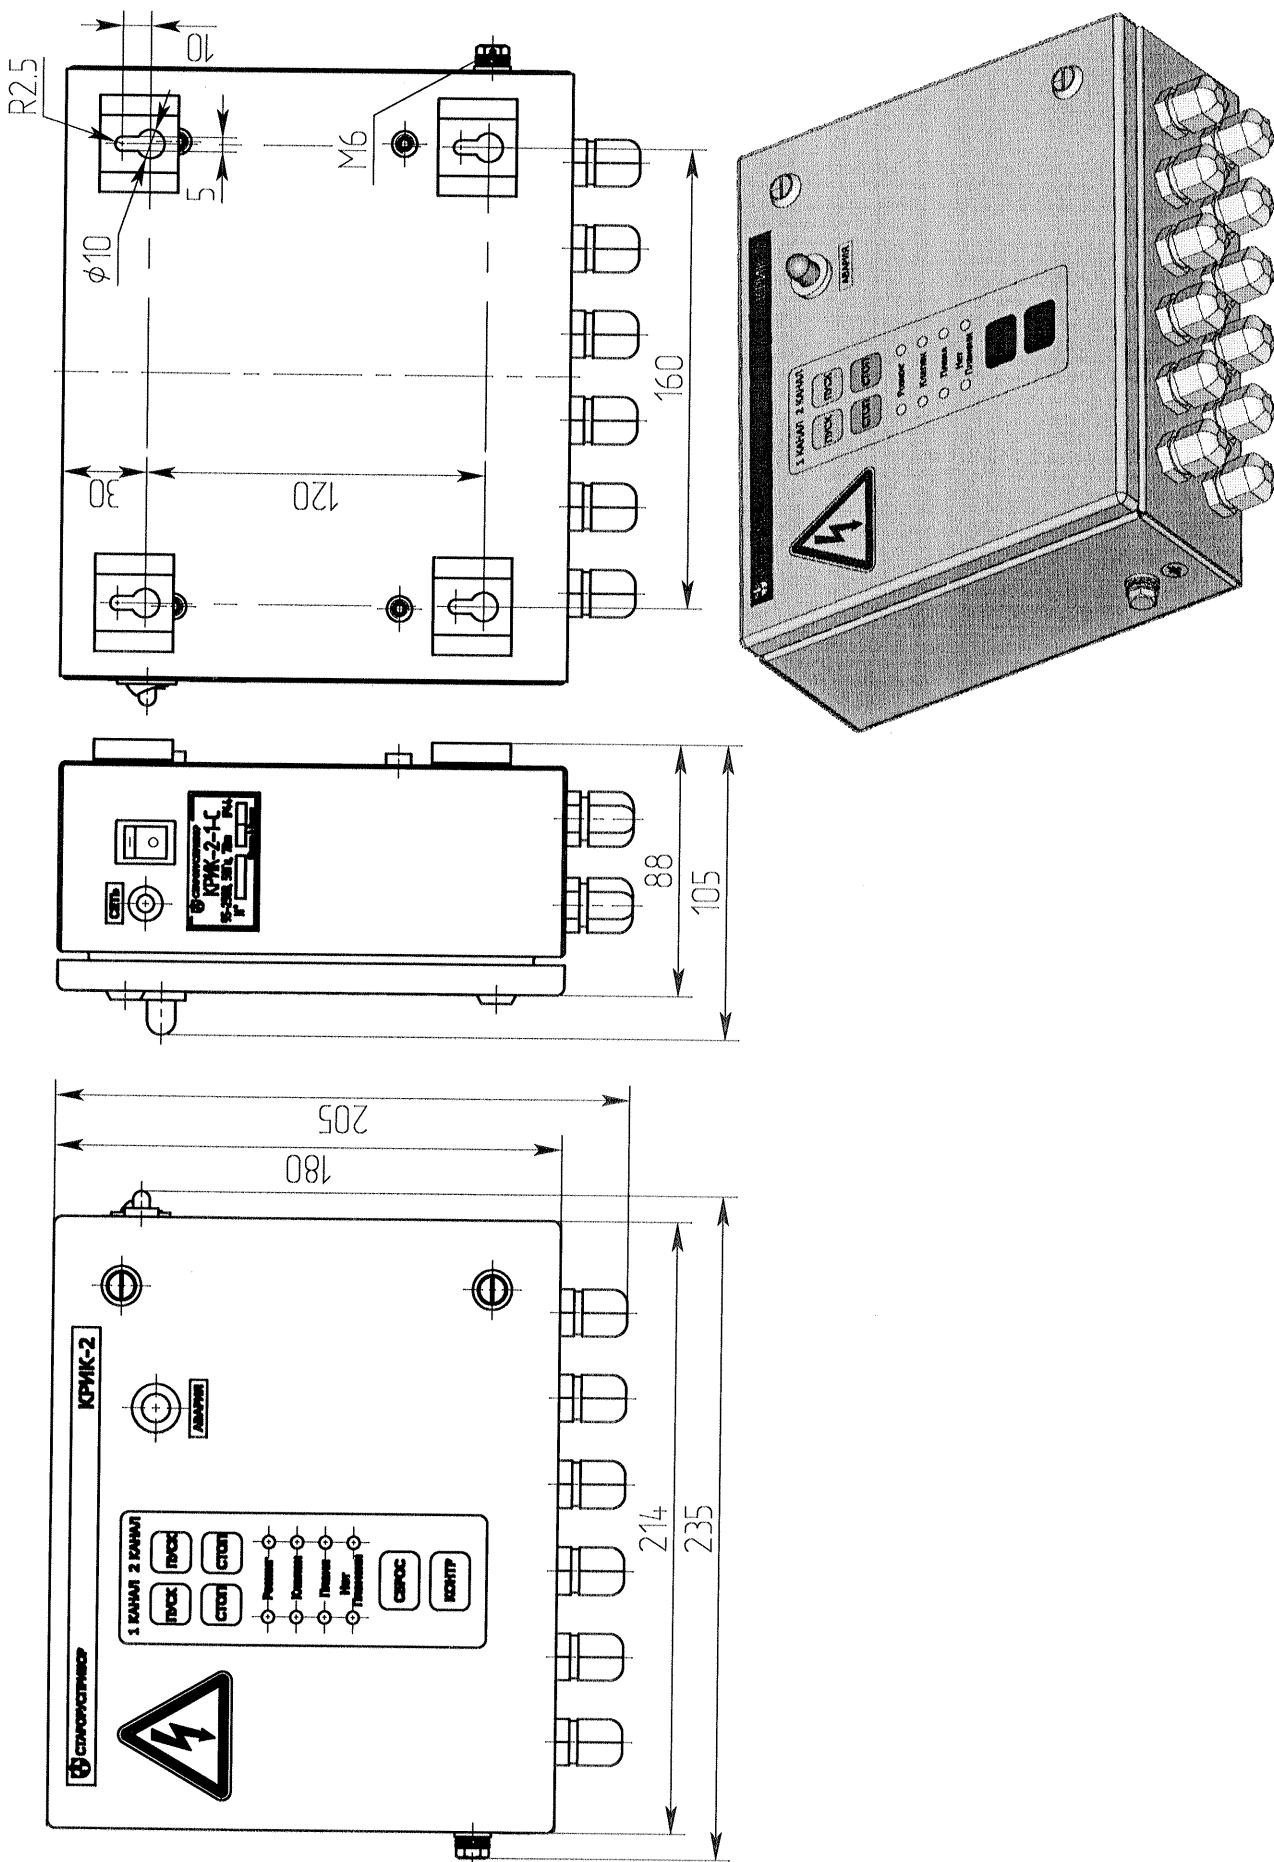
Внешний вид, габаритные и установочные размеры прибора настенного исполнения
